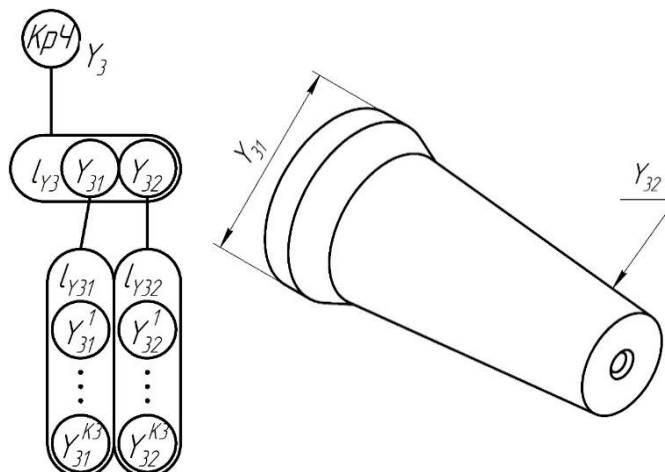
Ребро описывающее крепежную часть сборного шлифовального инструмента
